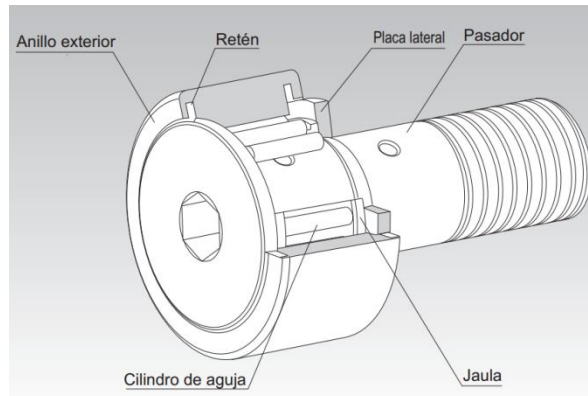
Partes de un seguidor de levas de rodillo cortesía (THK).
